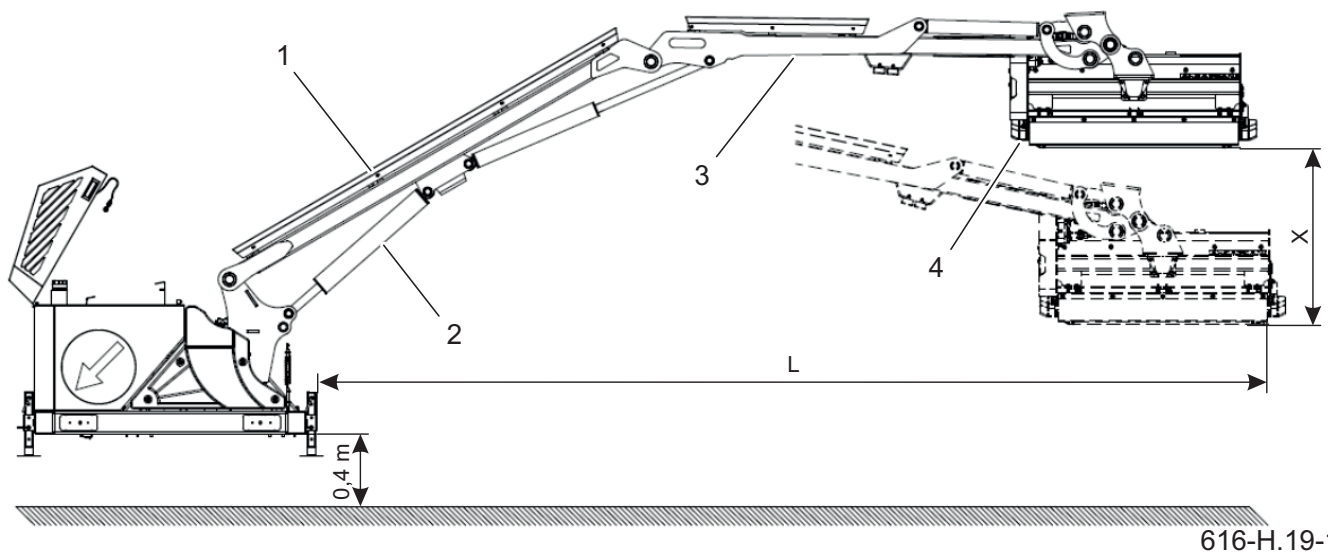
Przygotowanie przed uruchomieniem funkcji amortyzacji ramienia
